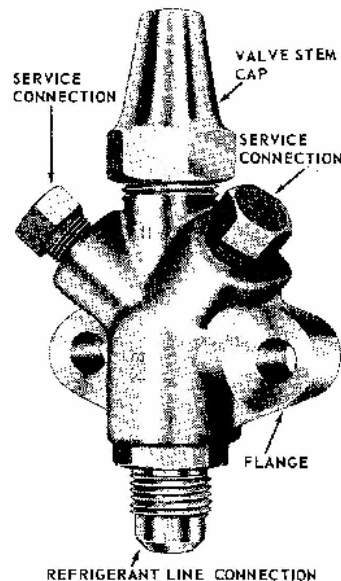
Pengaturan Posisi Katub service Kompresor
